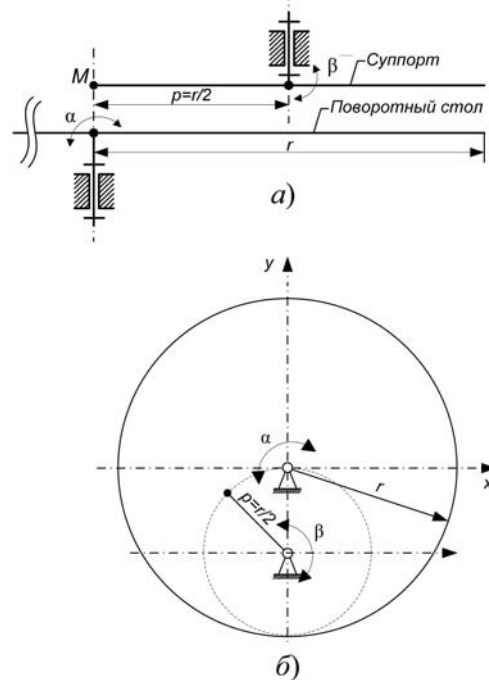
Кинематическая схема двухподвижного механизма с поворотным столом:
